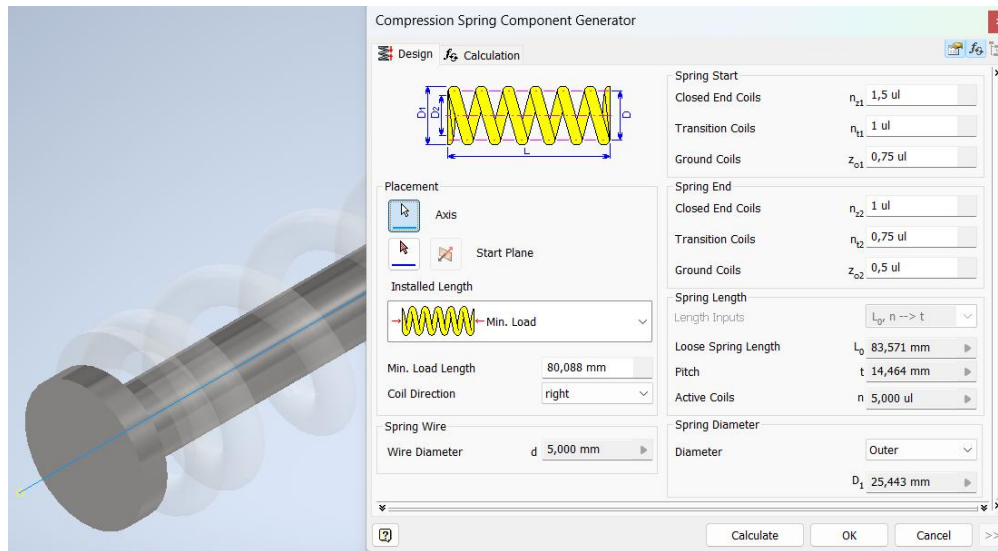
Вибір осі розташування пружини Compression Spring
